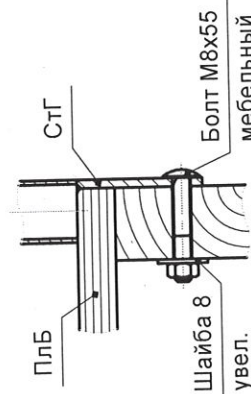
Крепление стяжки над горкой (СтГ) к площадке башни (ПлБ)
